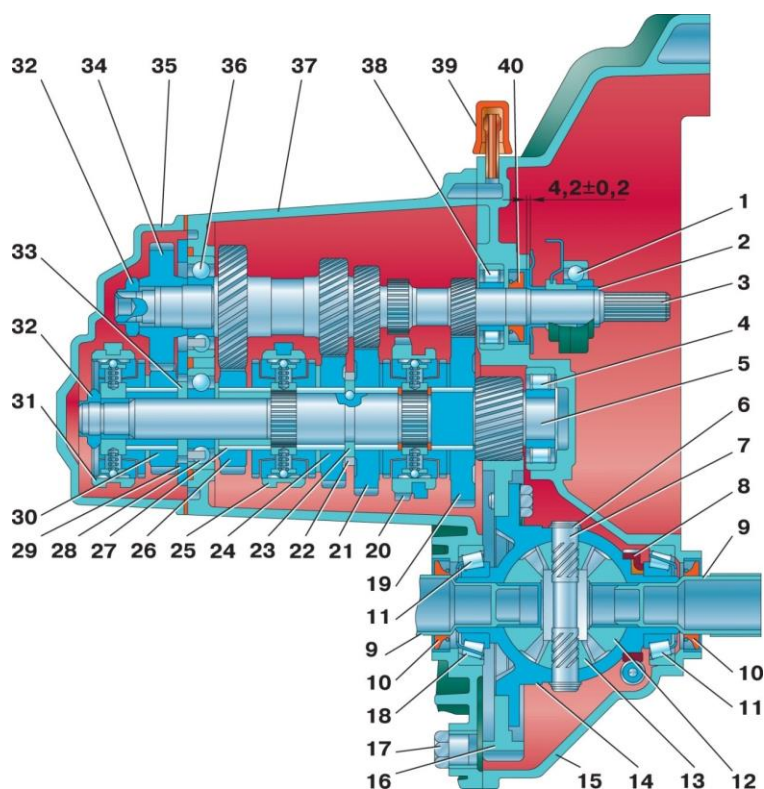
Коробка передач легкового автомобиля LADA «Samara».
